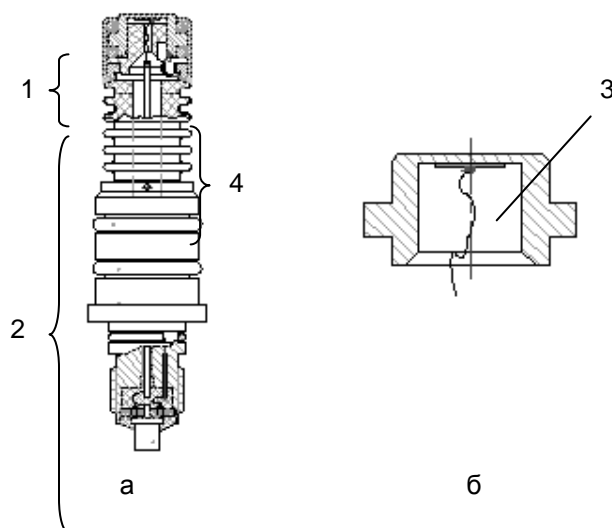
Конструкция датчика: а – общий вид датчика; б – конструкция излучателя
